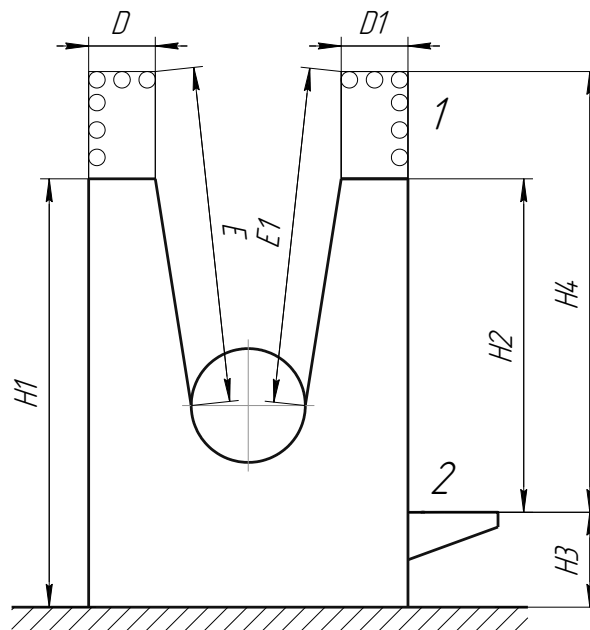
Безпечна конструкція вовчка із відкритим бункером, захисною решіткою та нерухомим щаблем: 1 – світловий бар'єр або знімна захисна решітка;
